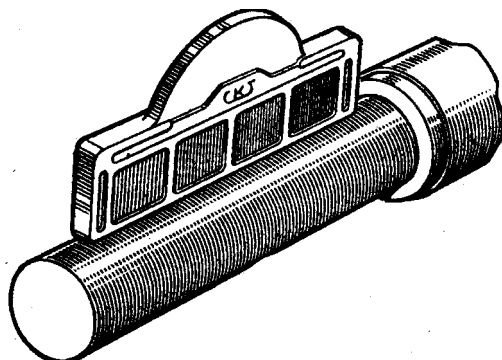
Контроль шероховатости поверхности вала с помощью образцов шероховатости
